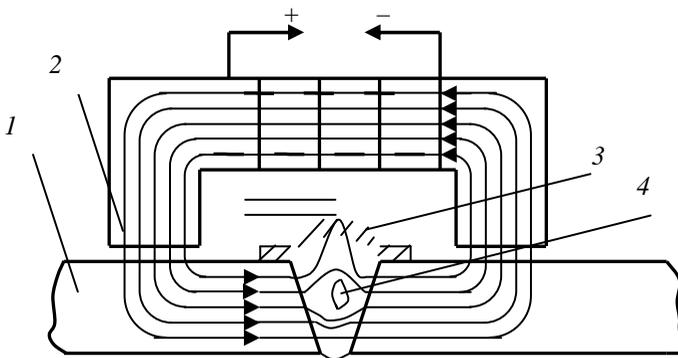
Схема проведения магнитографического контроля сварного шва:
